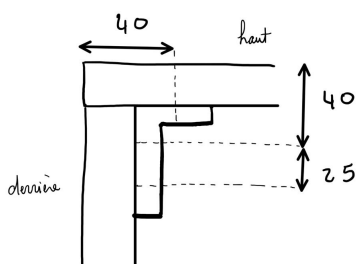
Fixation de la plaque de derrière à la plaque du haut
